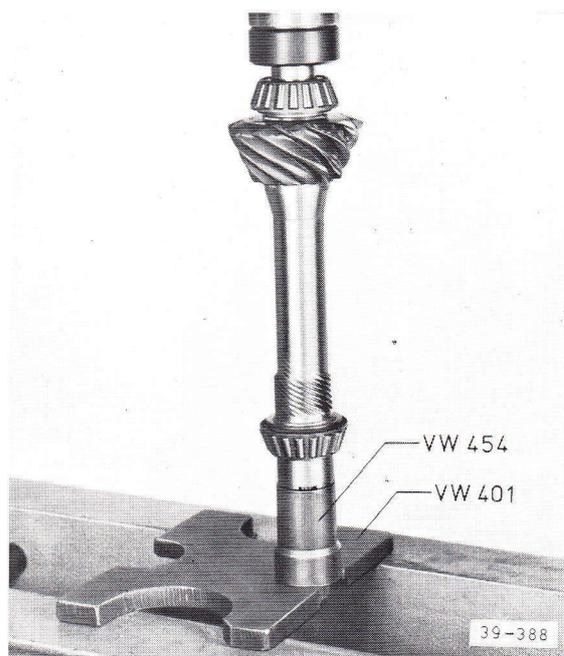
Bague intérieure de roulement à rouleaux coniques et douille pour bagues-joints, chauffer à 100° C, mettre en place sur le pignon d'attaque et finir d'emmancher à la presse.
